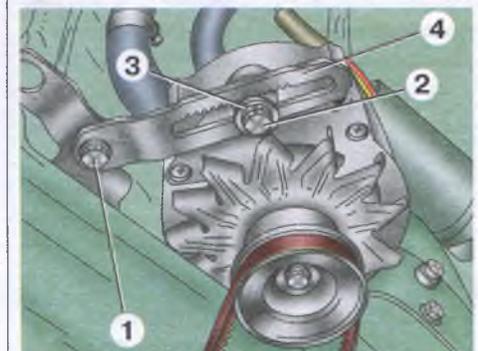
Механизм натяжения ремня привода генератора: 1 – болт крепления кронштейна; 2 – болт механизма натяжения; 3 – гайка регулировочная механизма натяжения; 4 – кронштейн механизма натяжения
